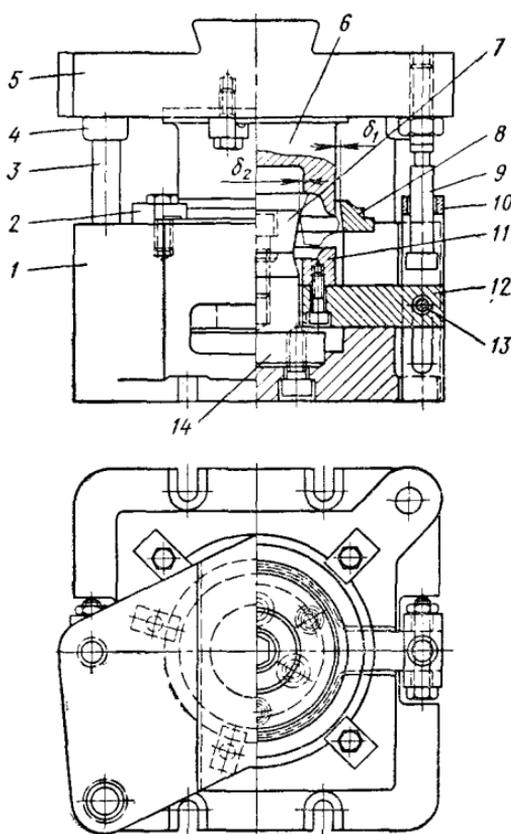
Совмещенный штамп для обрезки-прошивки с тягами:
